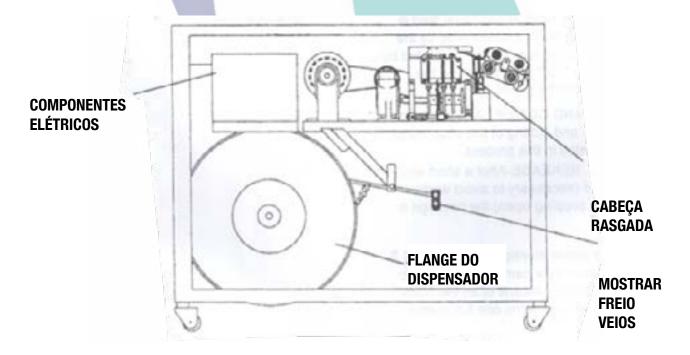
COMPONENTES PRINCIPAIS, VISTAS FRONTAL
